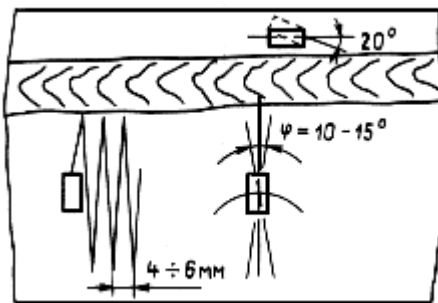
Схема сканирования при ультразвуковом контроле сварного шва
